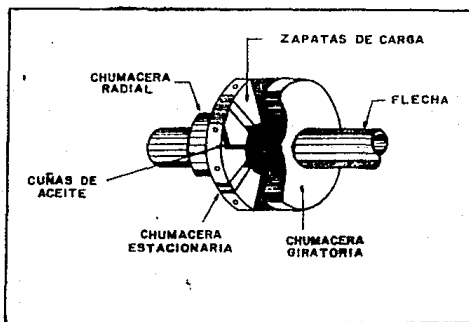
PARTES QUE INTEGRAN LA CHUMACERA AXIAL.
